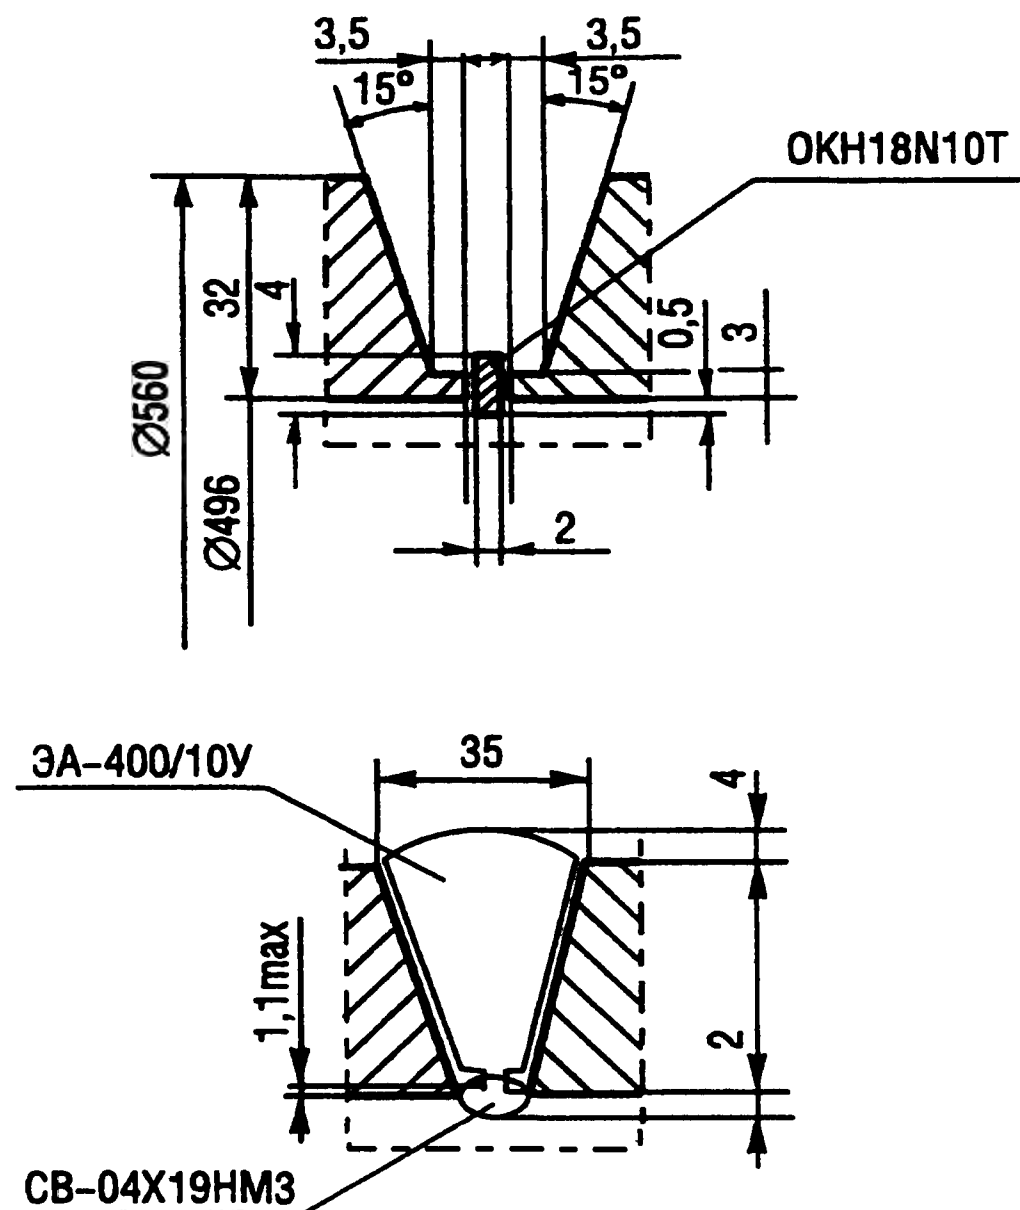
Разделка и сварка поперечного однородного сварного шва ГЦТ
